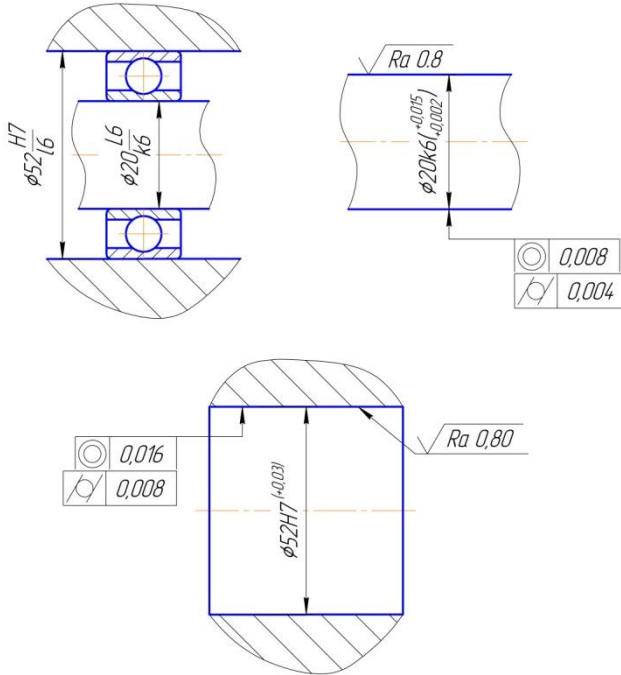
Ескізи підшипникового вузла, корпусу і вала
